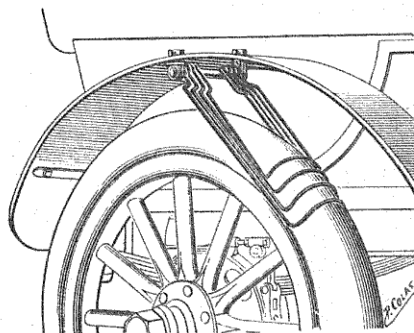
Un type d'arrache-clous pour roues arrière.
